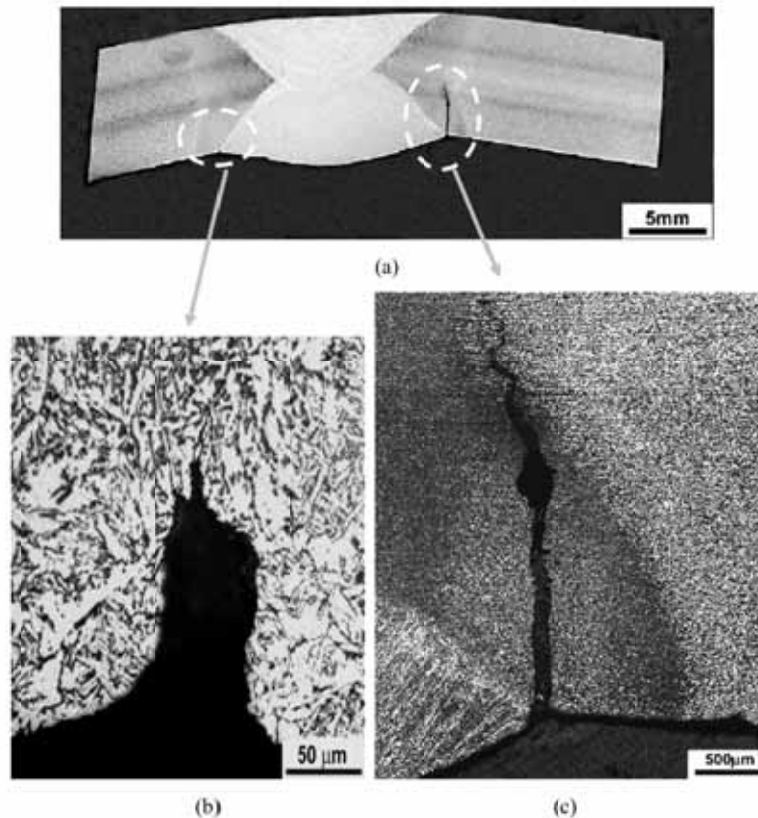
Corte transversal, grieta pasante: (a) Examen macroscópico; (b) Superficie interna del tubo con $100 \mu\text{m}$ de profundidad. Se observa la grieta siendo nucleada en la raíz de este defecto; (c) Superficie interna del tubo. La Grieta es nucleada en la interface entre la ZAC y el cordón de soldadura y el camino de propagación de la grieta es independiente del gradiente macro y microestructural. Ataque: Nital. MO [248].
